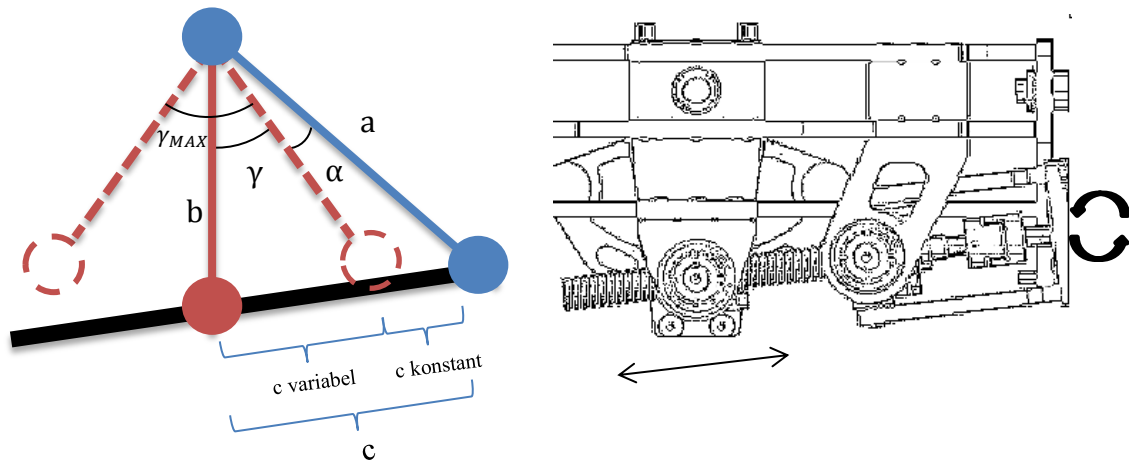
Översiktsbild av plattformens konstruktion och utseende, [13]
